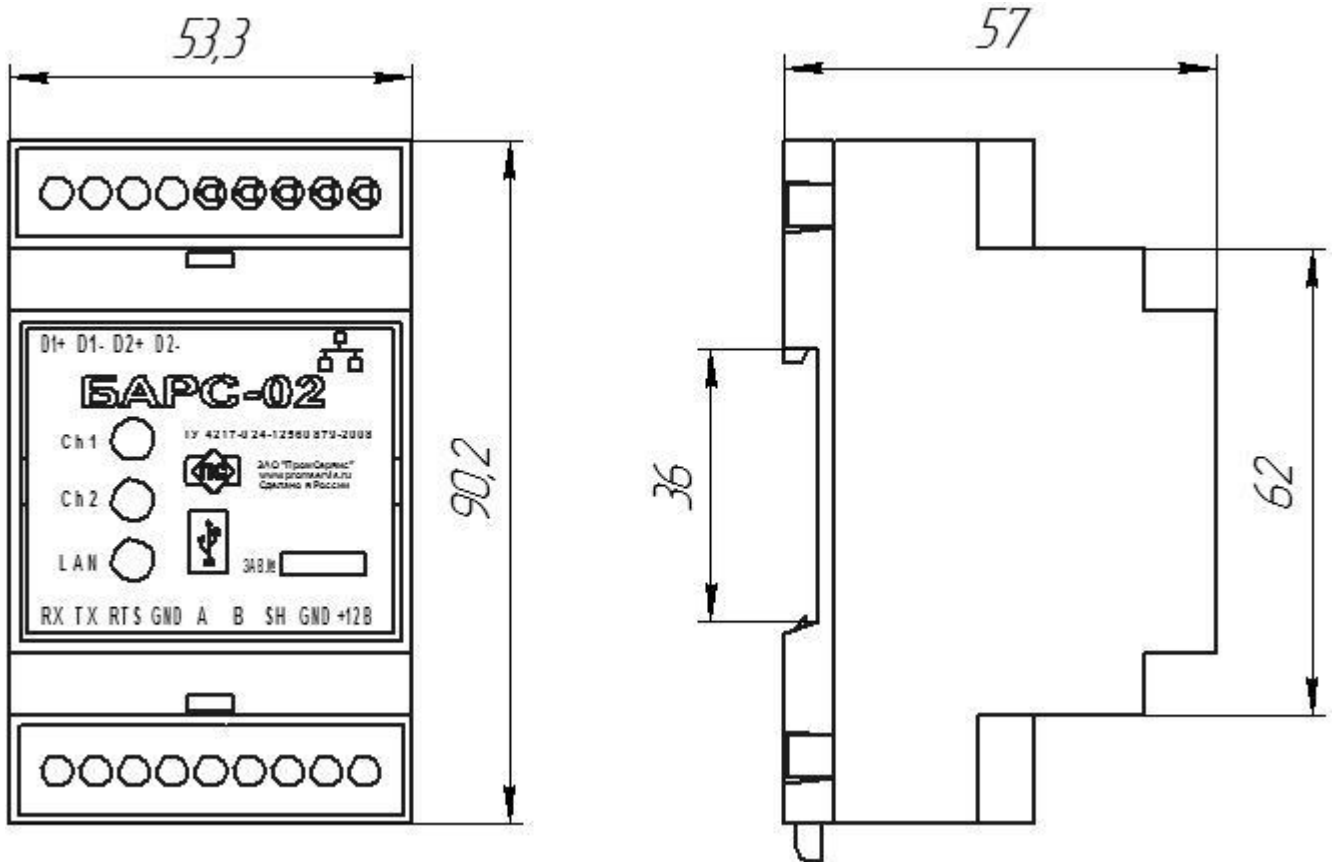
Габаритные и присоединительные размеры BARC-02-П-3-П
